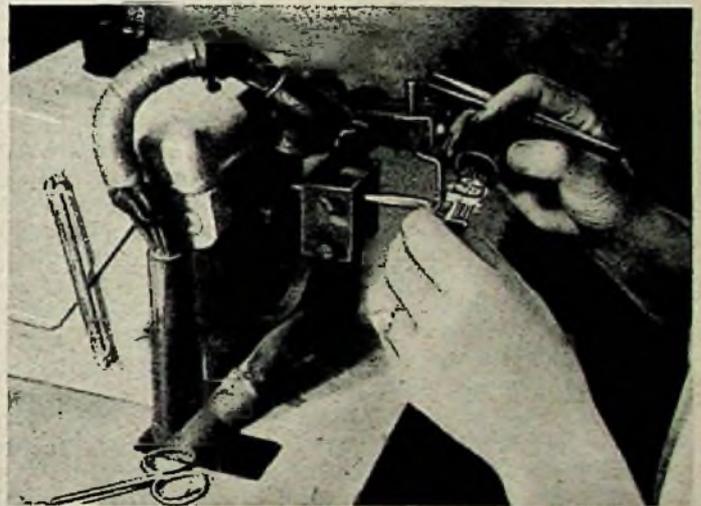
Röhrenmontage. Man sieht die Punktschweißmaschine und das Werkzeug, das für den Zusammenbau benötigt wird
